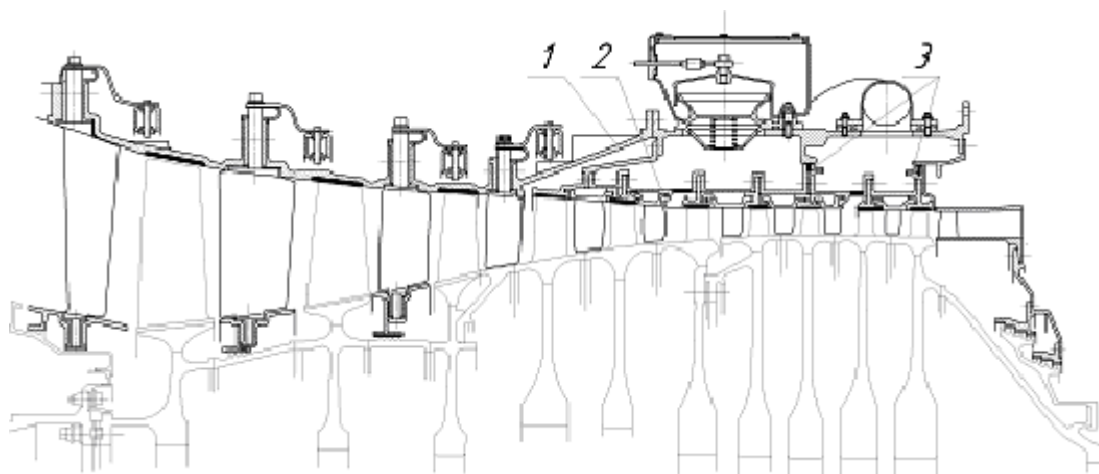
Корпус с двойной стенкой компрессора ВД ТРДД V2500:
